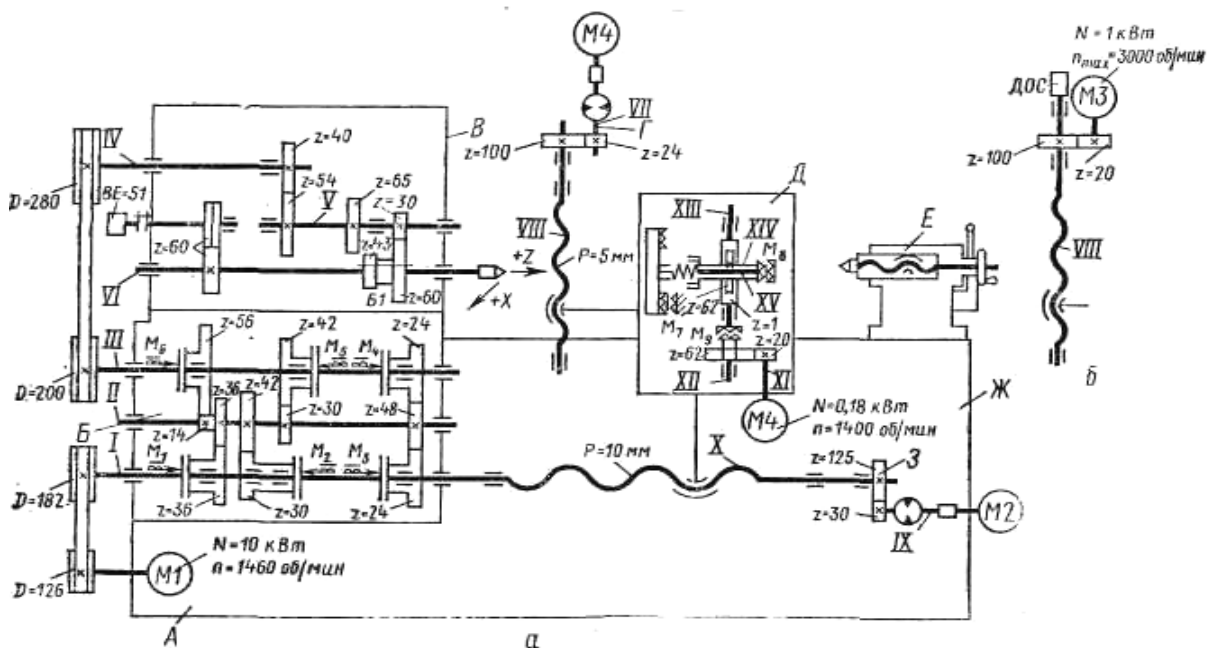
Кинематическая схема токарного станка с ЧПУ модели 16К20Ф3
